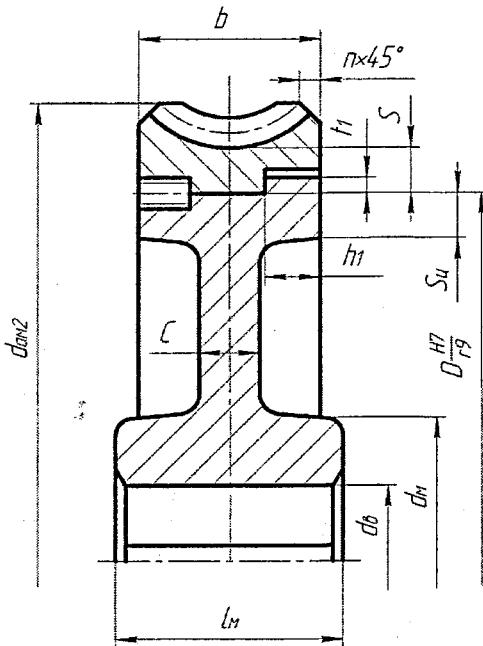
Конструктивні параметри (*constructive parameters*) черв'ячного колеса
